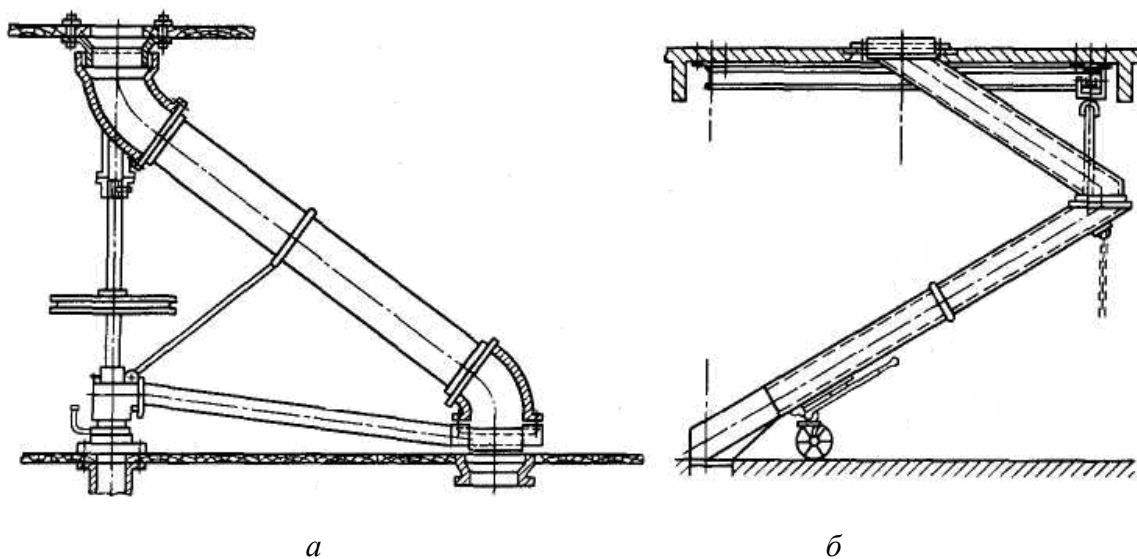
Поворотные спуски (трубы) для подачи насыпного груза
